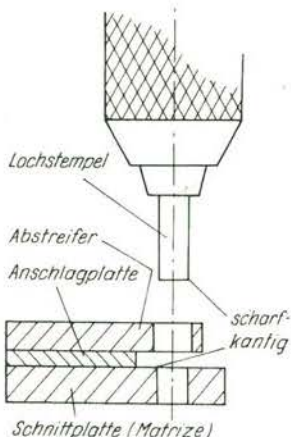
Prinzipzeichnung eines Behelfs-Lochwerkzeugs. Die Abstreiferplatte kann bei entsprechend ausgeführter Bohrung auch als Führungsplatte für den Lochstempel dienen.
